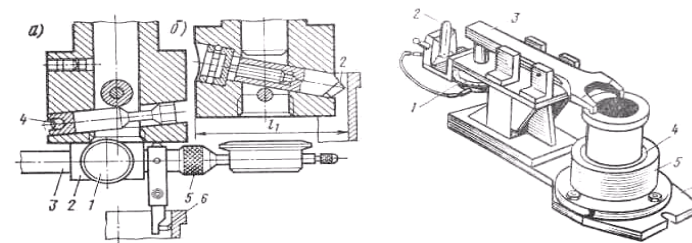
Резцовая головка станка 2А78Н с приспособлениями для центрирования гильз (а) и установки резца (б)
